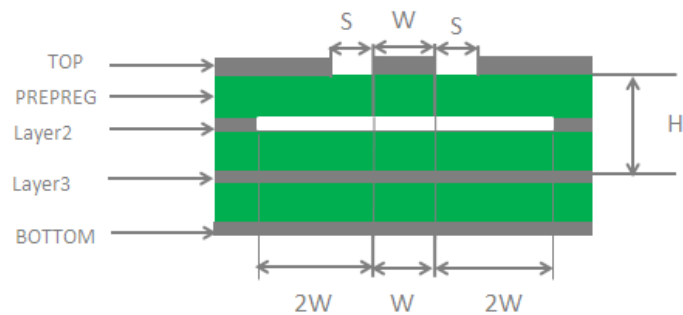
：四层 PCB 板共面波导结构（参考地为第三层）
